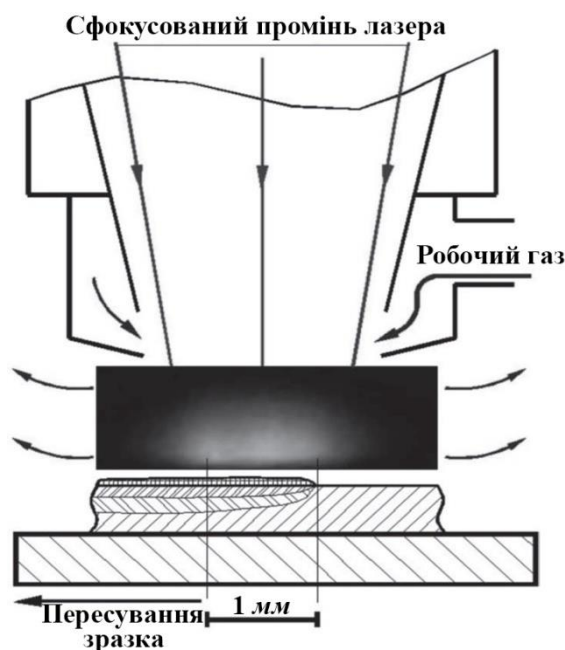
Схема лазерно-плазмової обробки металу із зображенням приповерхневої плазми оптичного пульсуючого розряду
